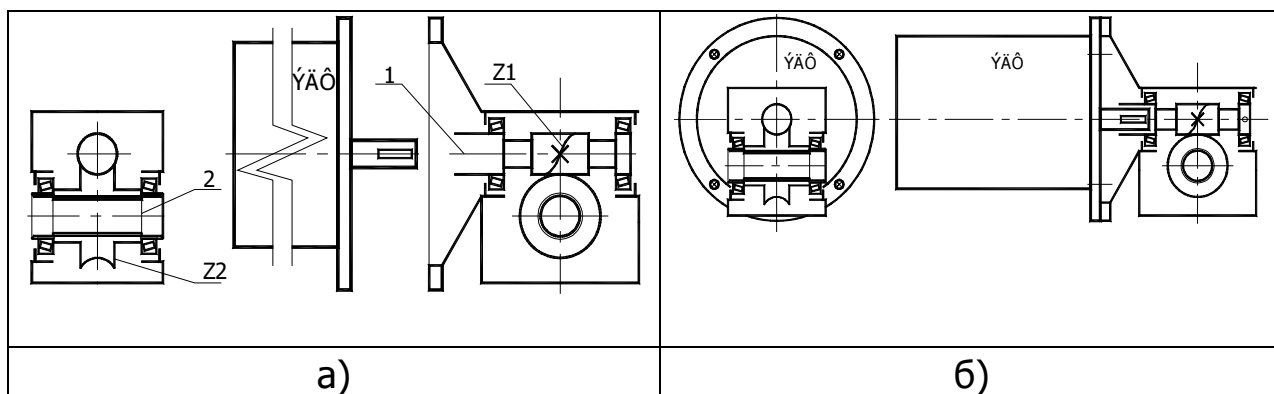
Схема червячного редуктора с полыми валами для сборки мотор-редуктора. ЭДФ – электродвигатель фланцевого исполнения.
